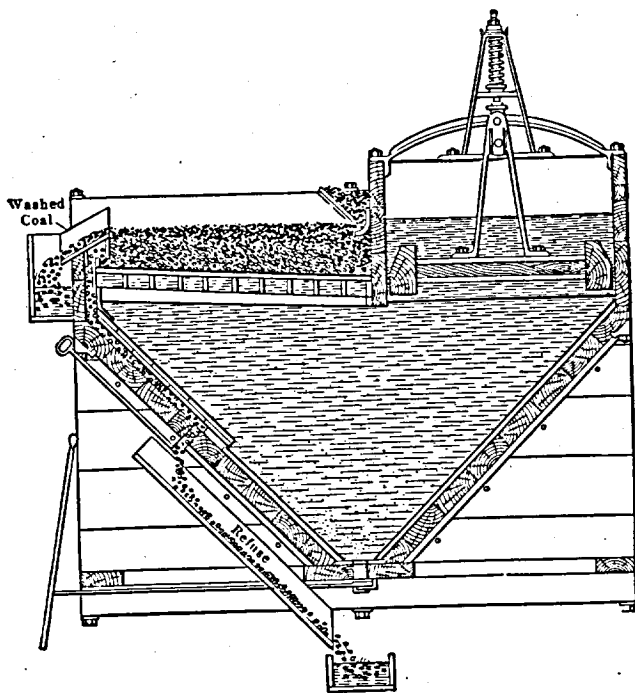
Coupe verticale: jig à gaillettes New Century.
